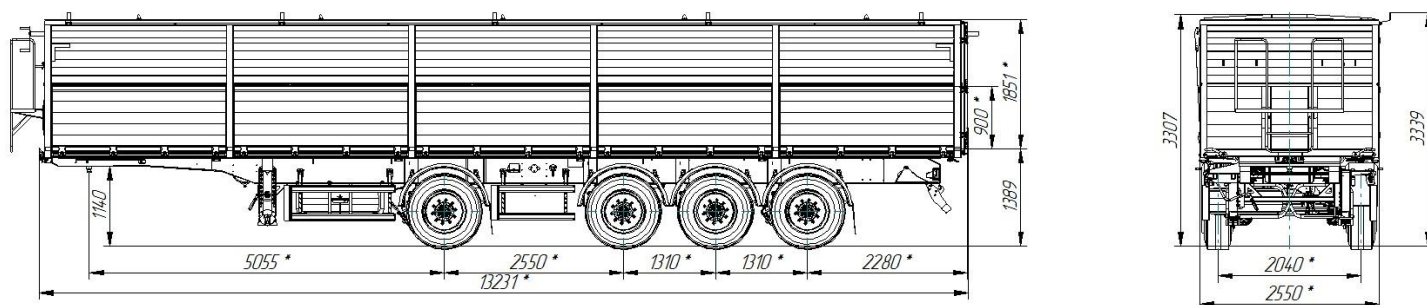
Полуприцеп бортовой модели 924941-160. Тип кузова зерновоз
